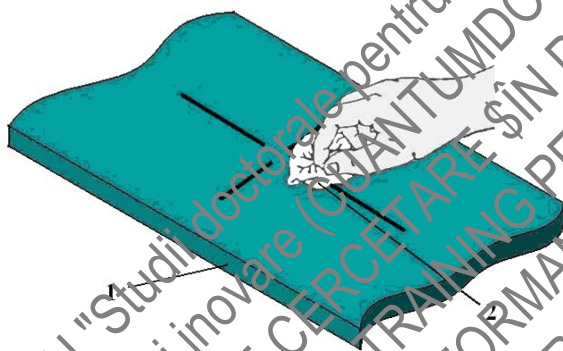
Îndepărtarea excesului de substanță de marcă cu alcool izopropilic s.a.: 1- piesă (structură); 2- lavetă
